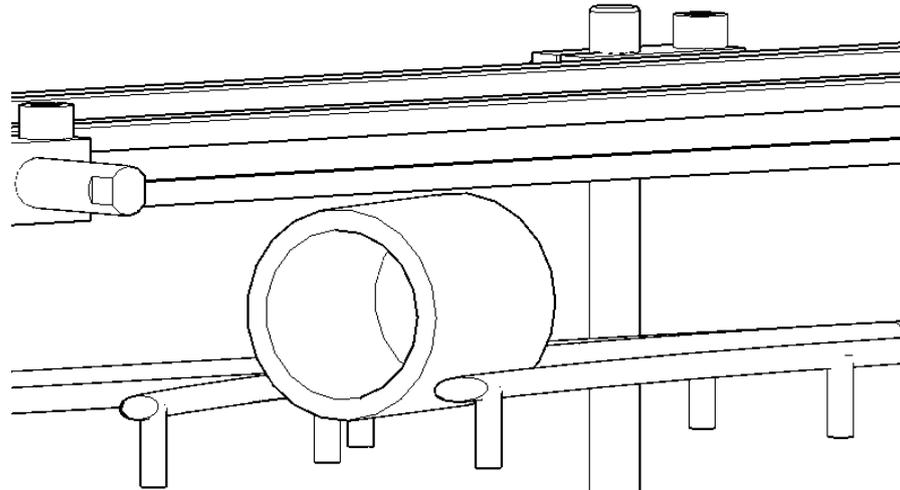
Vista del pistón en posición horizontal siendo desviado. Fuente: elaboración propia.
